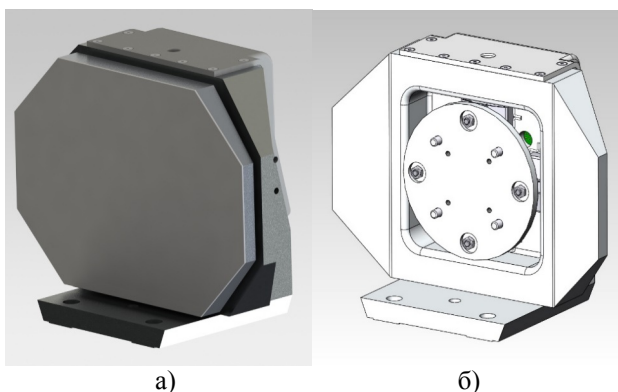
Пьезоплатформа: а — общий вид; б — неподвижная часть пьезоплатформы
